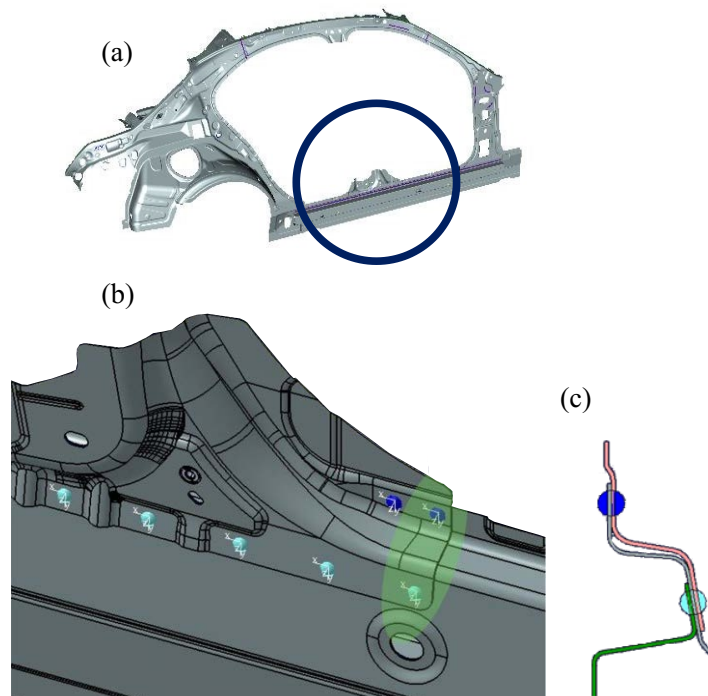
(a) Fügeelementposition, (b) Sicht auf Schweißpunkte, (c) Schnitt
